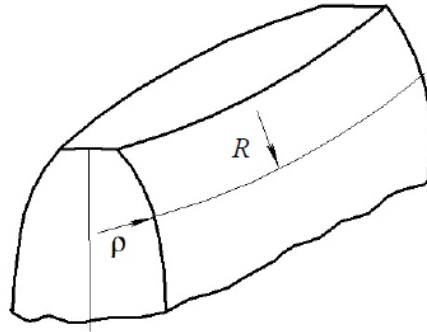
Зуб шестерни с криволинейными образующими боковых поверхностей
